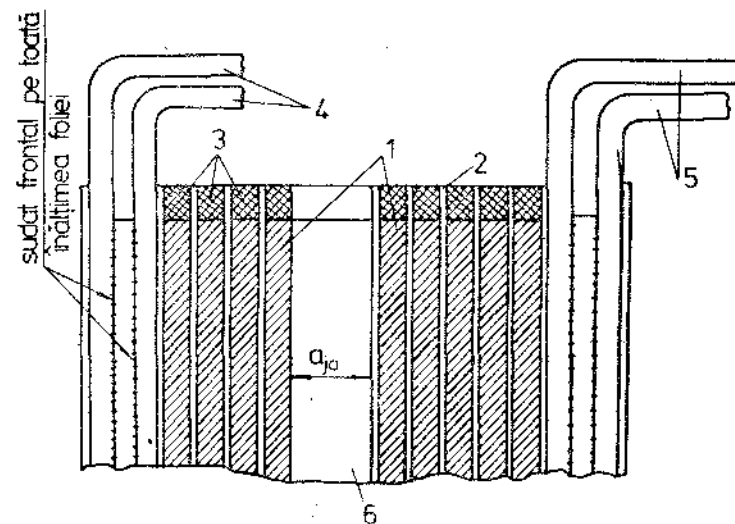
29. Înfășurare cilindrică stratificată din folie de AluminIU:
